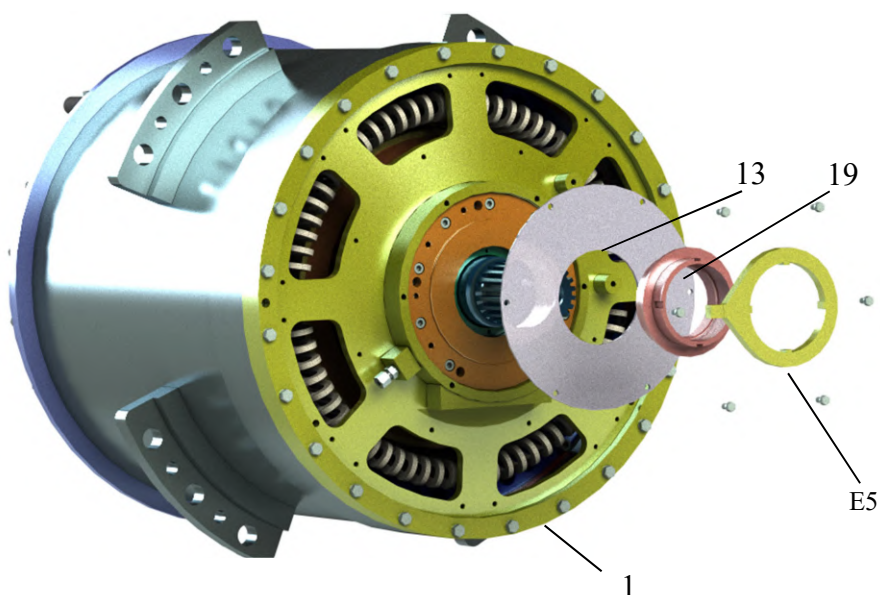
Демонтаж упора со стороны привода и крышки.
